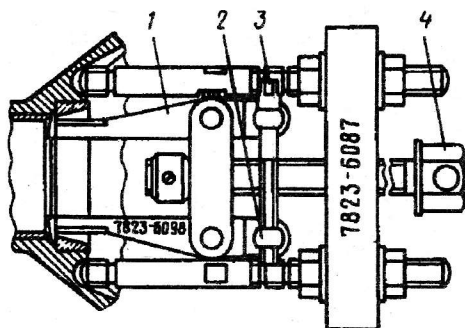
Выпрессовка наружного кольца подшипника коробки дифференциала из картера заднего моста:
